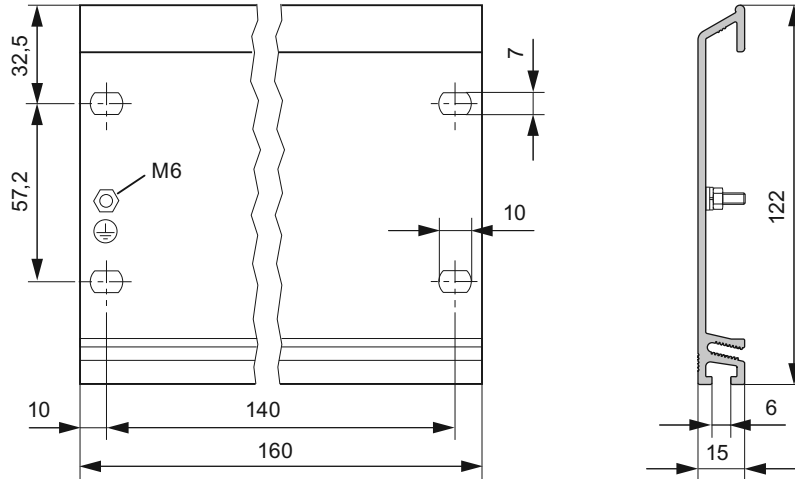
Croquis acotado del perfil soporte en ancho estándar de 160 mm
